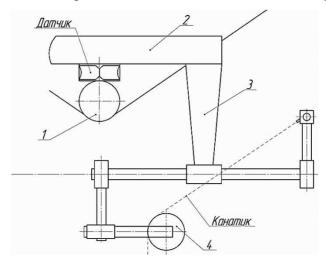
Схема консольной конструкции канатиковой заправки: 1 – измерительный вал; 2 – консоль станины; 3 – конструкция, поддерживающая ролик;
